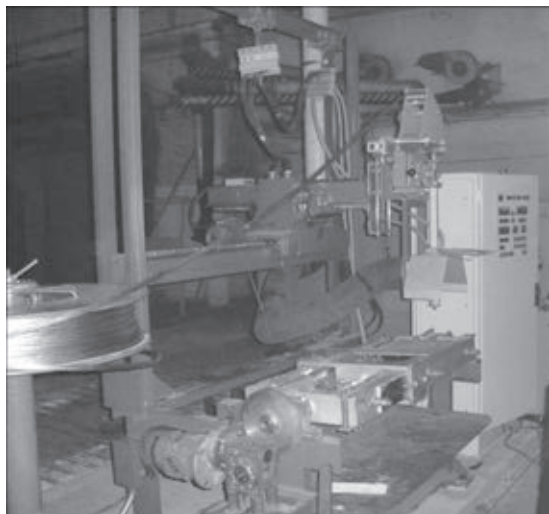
Установка УД-298М для наплавки ножей горячей резки
